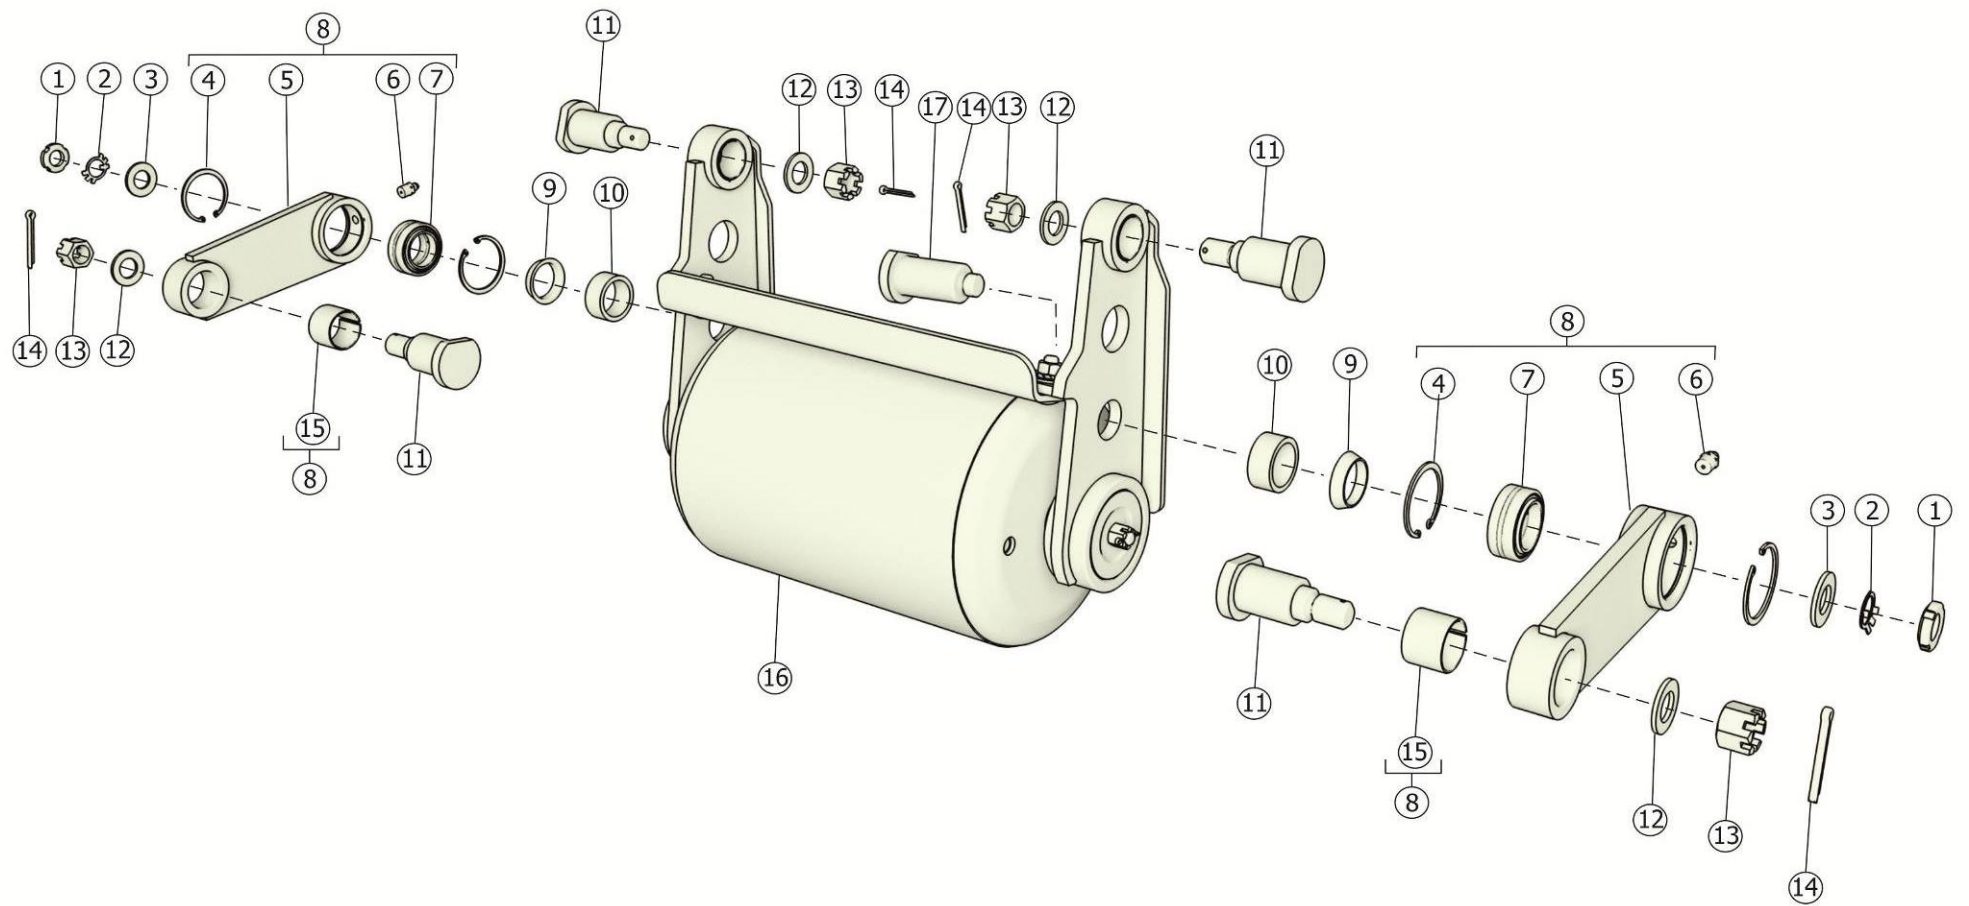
Установка ролика опорного ПК-300.01.06.000Б
